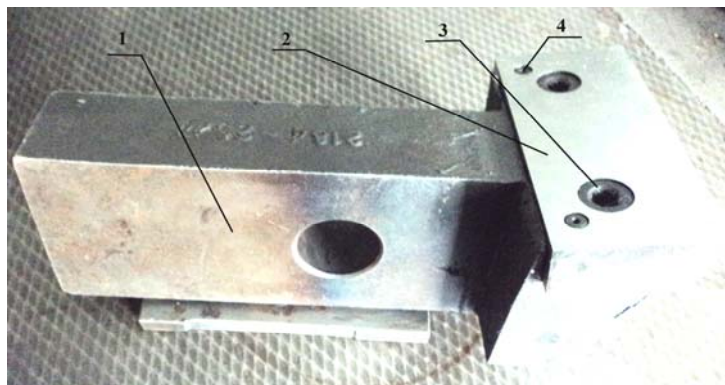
Долбежный резец с механическим креплением режущей пластины:
